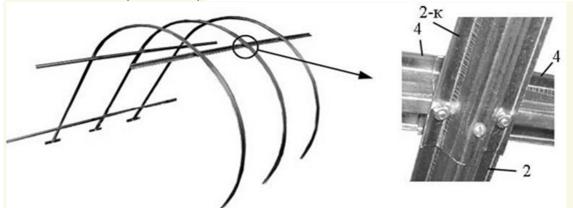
Присоединить детали №2 и №2-к с замечанием для 4 этапа сборки.
